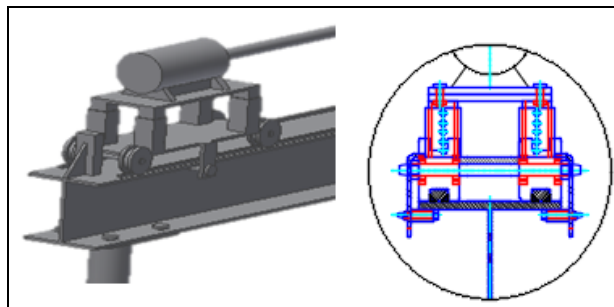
Carro Monorraiel de Lavado Interno con Soporte de Viga HEA
